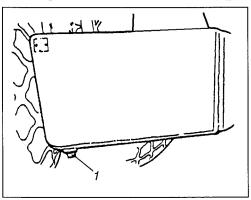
Réservoir à carburant 1 bouchon de vidange
